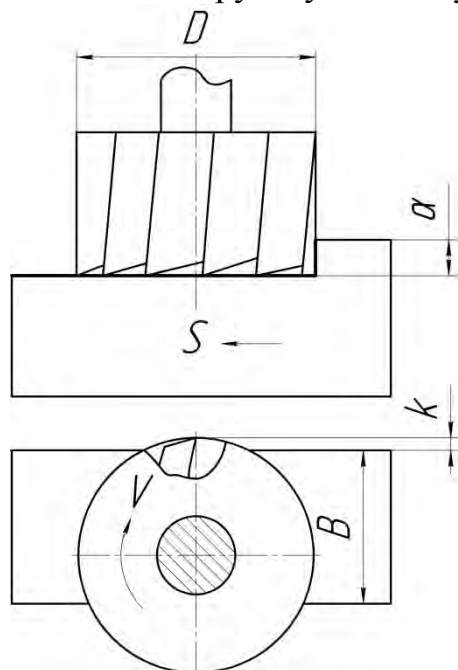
Схема фрезерования наклонной плоскости
